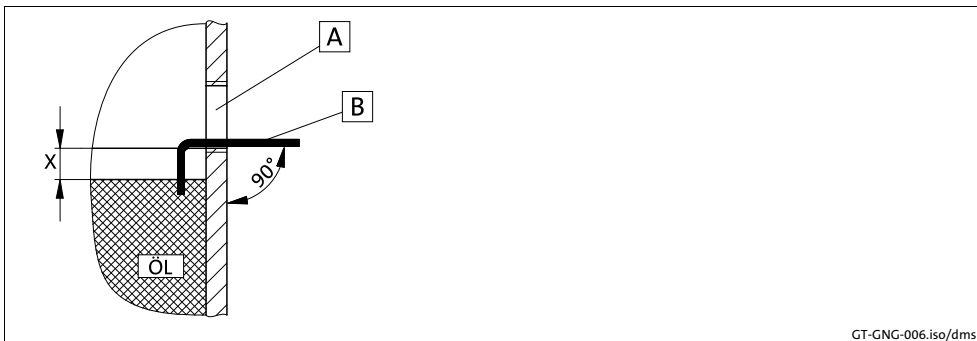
Ölstandkontrolle mit Hilfswerkzeug
